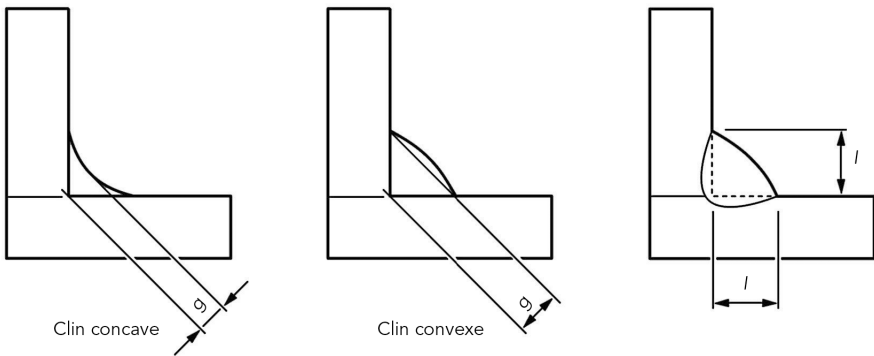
Gorge (g) et largeur/hauteur (l) du cordon d'une soudure d'angle.
